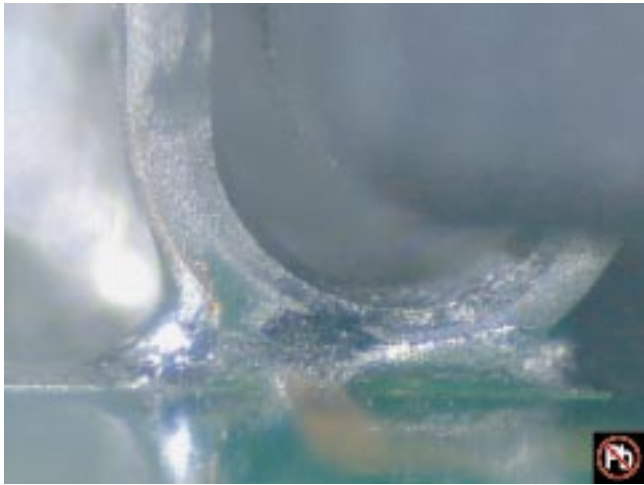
Soldadura SnAgCu; Proceso No-Lavable, Reflujo N2
